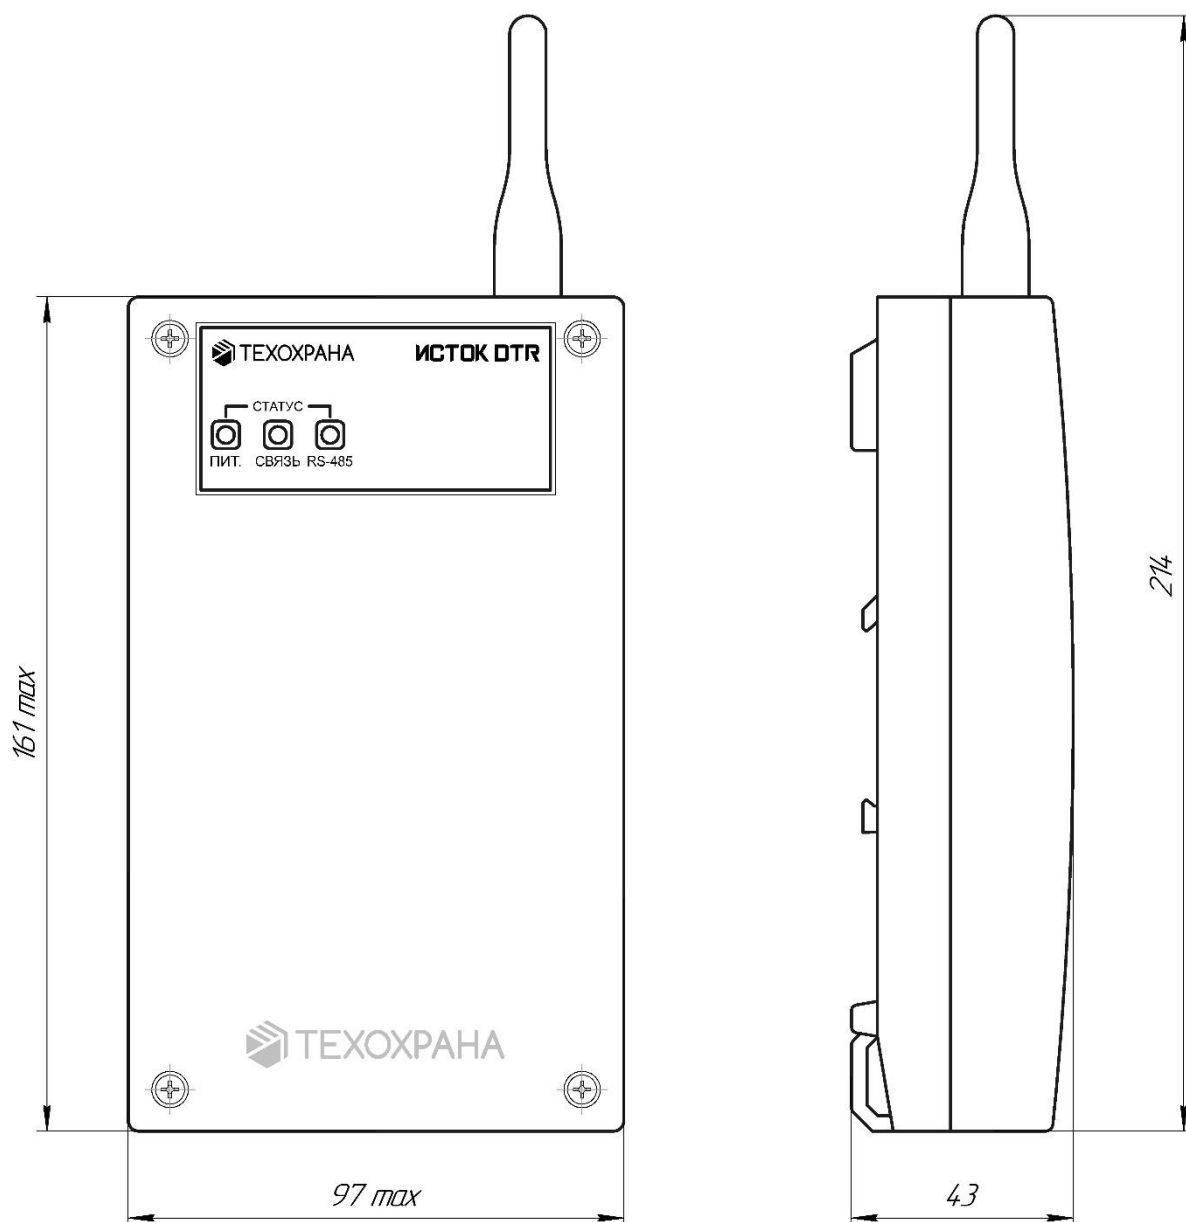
Габаритные размеры РТР «ИСТОК DTR»
